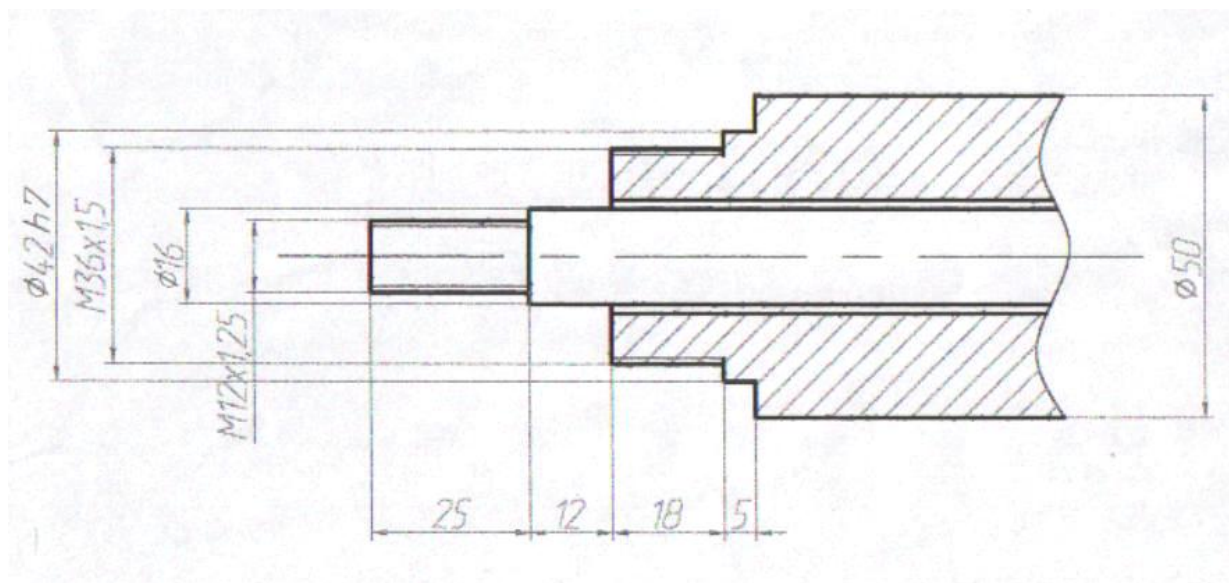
Присоединительные размеры руки манипулятора
